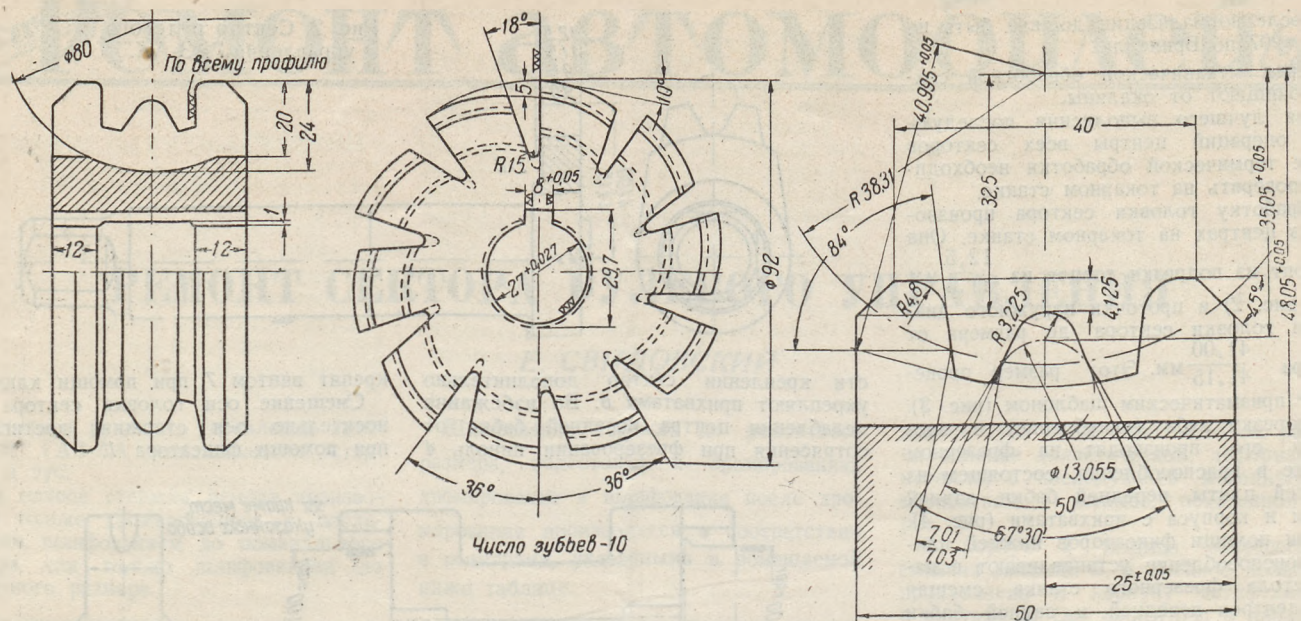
Фасонный фрез для фрезеровки зуба сектора рулевого управления.
